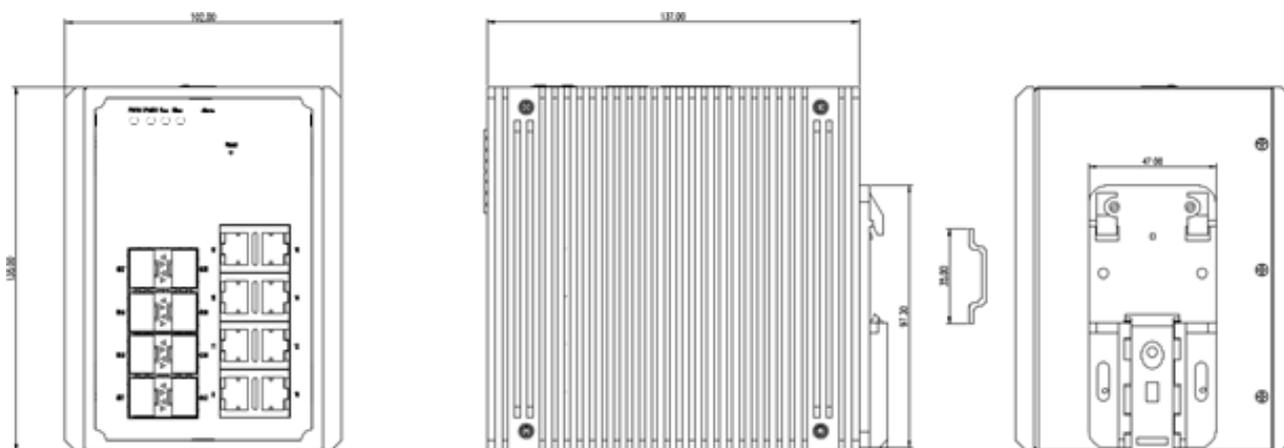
Габаритный чертеж корпуса «Тип 3» с креплением на DIN-рейку
